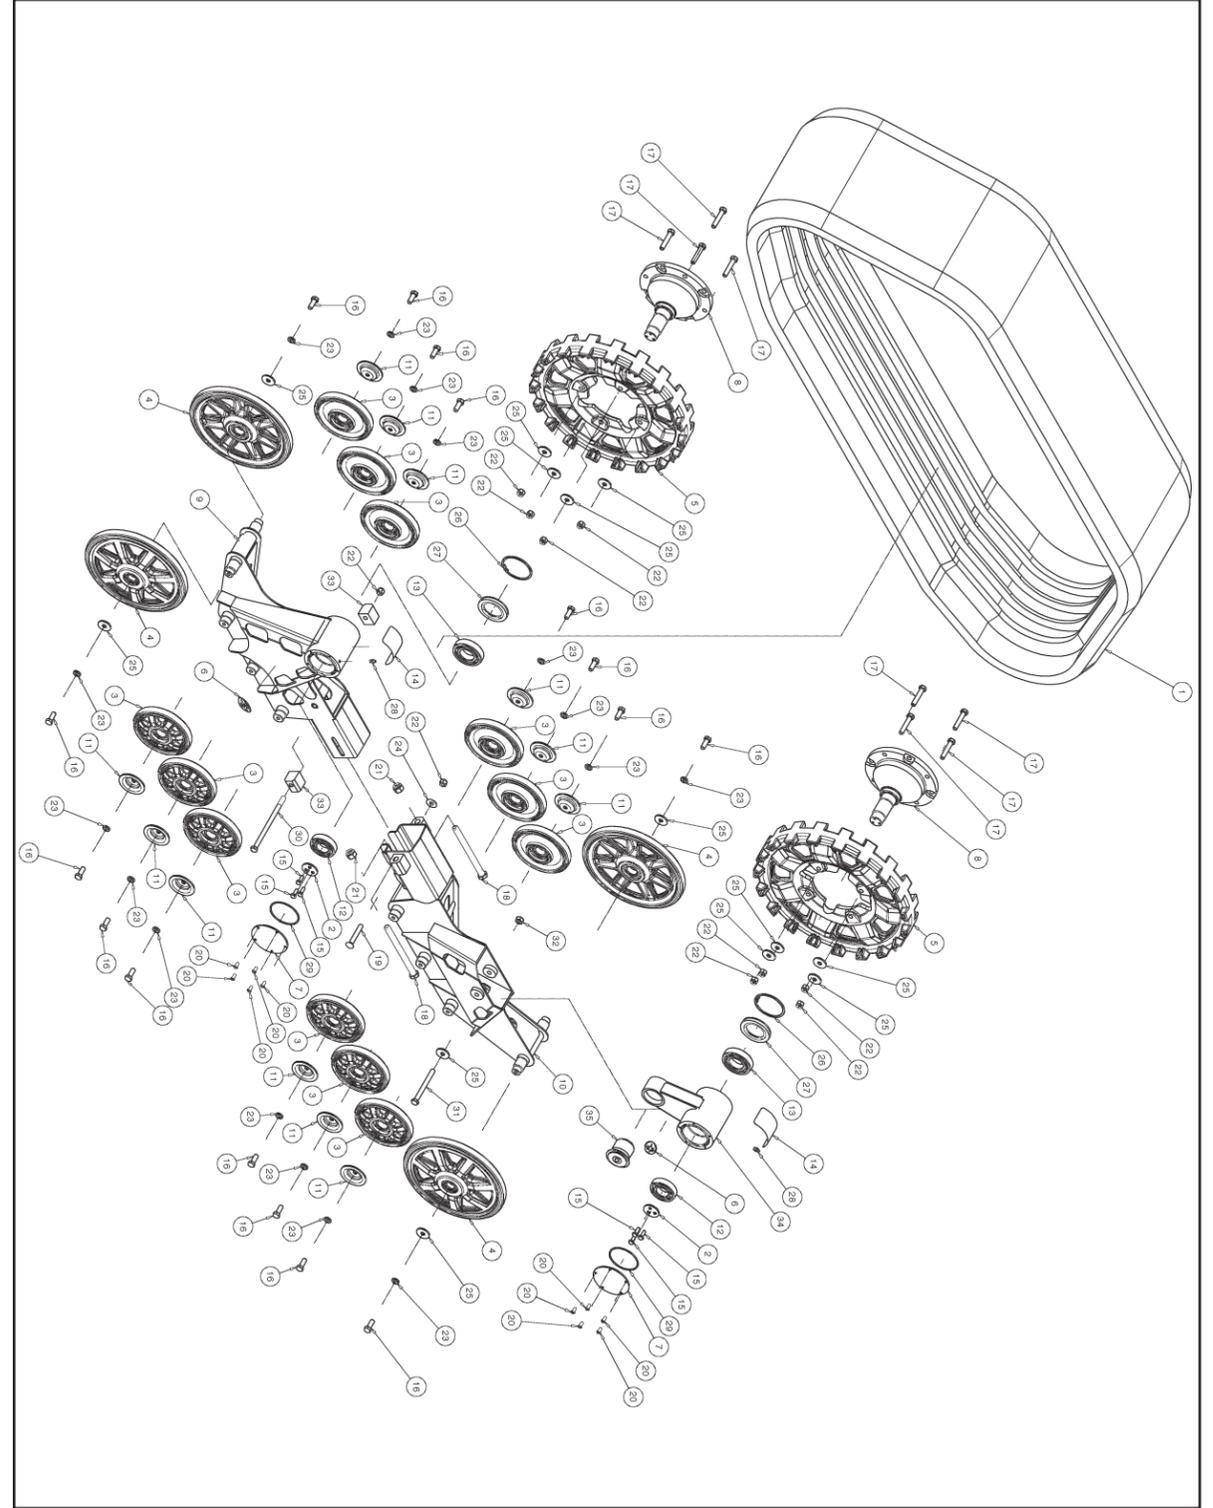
Vue explosée - Ensemble de chenille arrière droit
